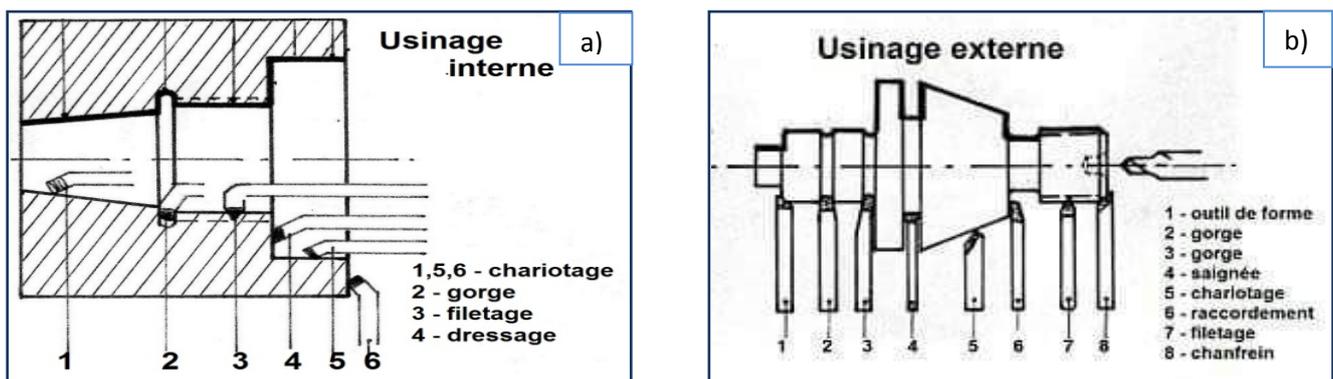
Principaux usinage par tournage : a) interne, b) externe. [15]
